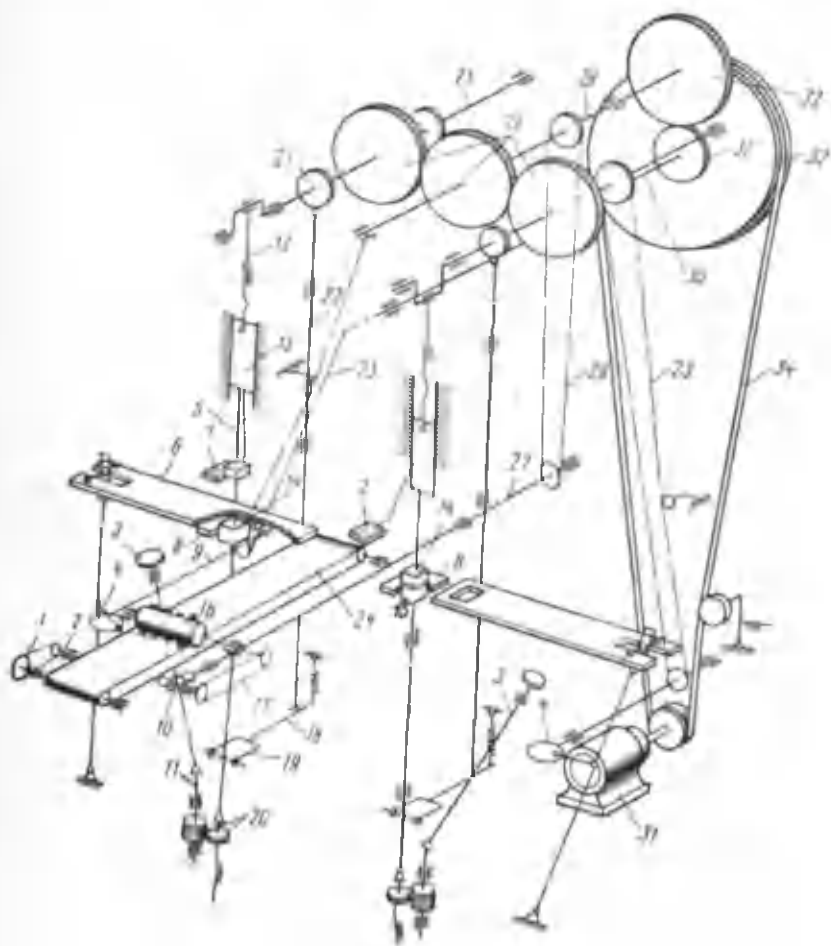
Кинематическая схема двухпуансонного пресса для изготовления агломератов галетных элементов батареи «Энергия»:
